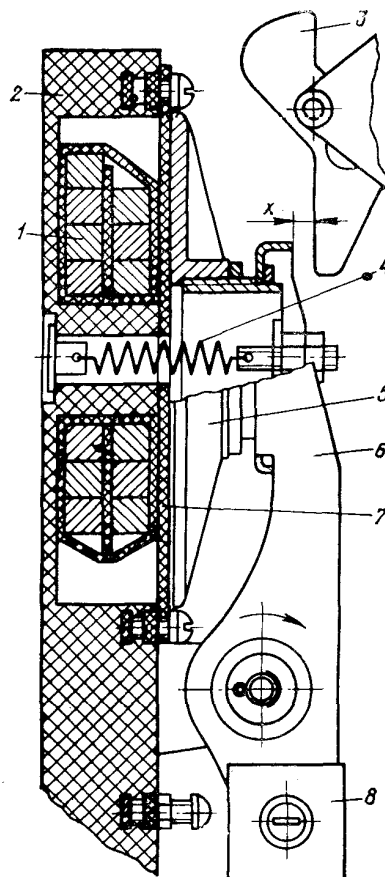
ІДМ, що впливає на спусковий пристрій, де 5 – диск; 6 – скоба; 8 – вантаж що врівноважує систему; 4 – утримуюча пружина; 7 – ізоляційна прокладка; 1 – індуктор; 2 – корпус; 3 – механічна засувка
